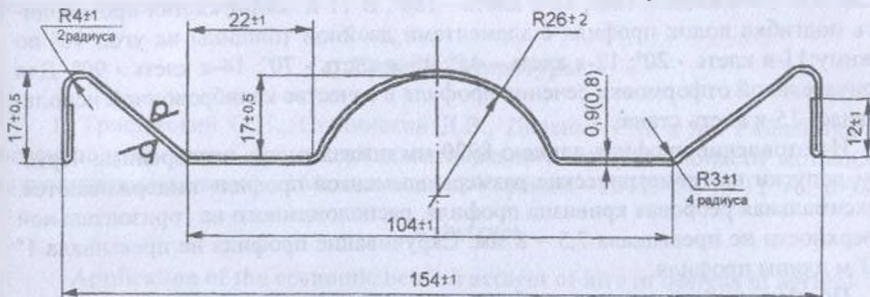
Специальный гнутый профиль лопасти мотовила жатки
